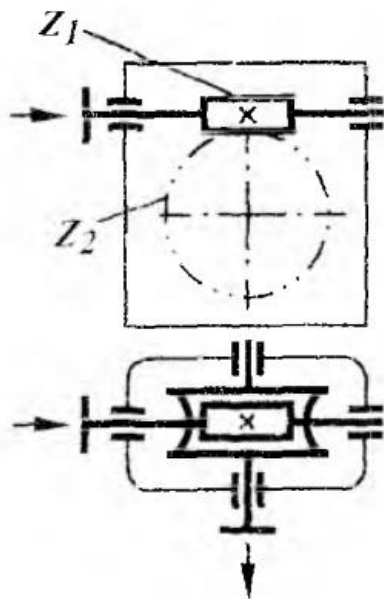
Черв'ячний з верхнім розташуванням циліндричного черв'яка
